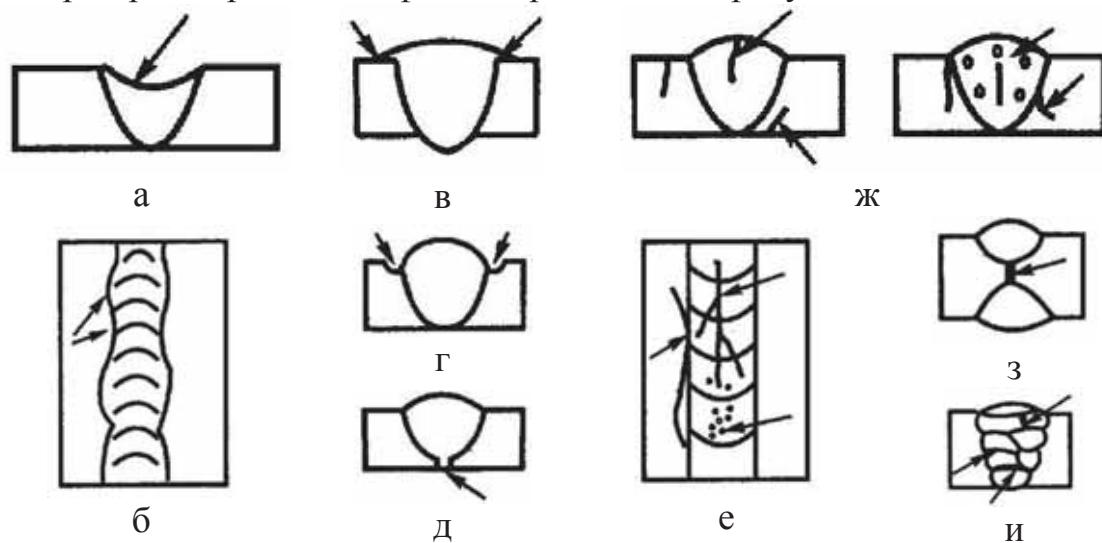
Виды дефектов сварных швов: а – ослабление шва; б – неравномерность ширины; в – наплыv; г – подрез; д – непровар; е – трещины и поры; ж – внутренние трещины и поры; з – внутренний непровар; и – шлаковые включения
